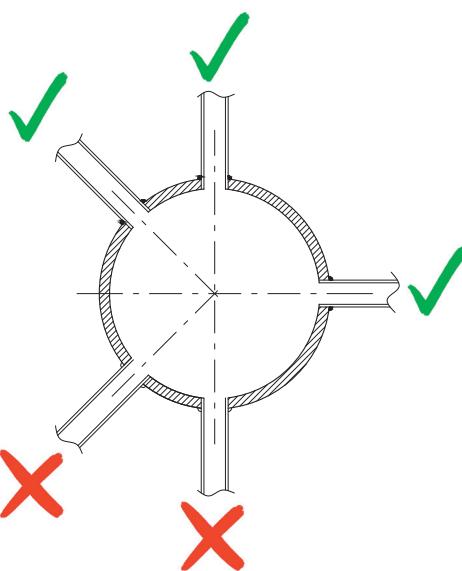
Conexiones soldadas de la tubería
